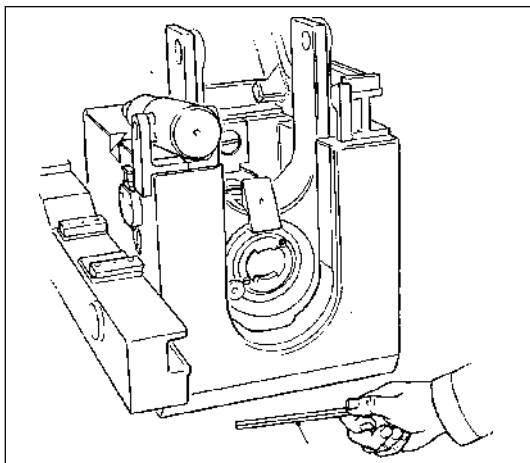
Colocação da barra de retenção da cunha L1A1
